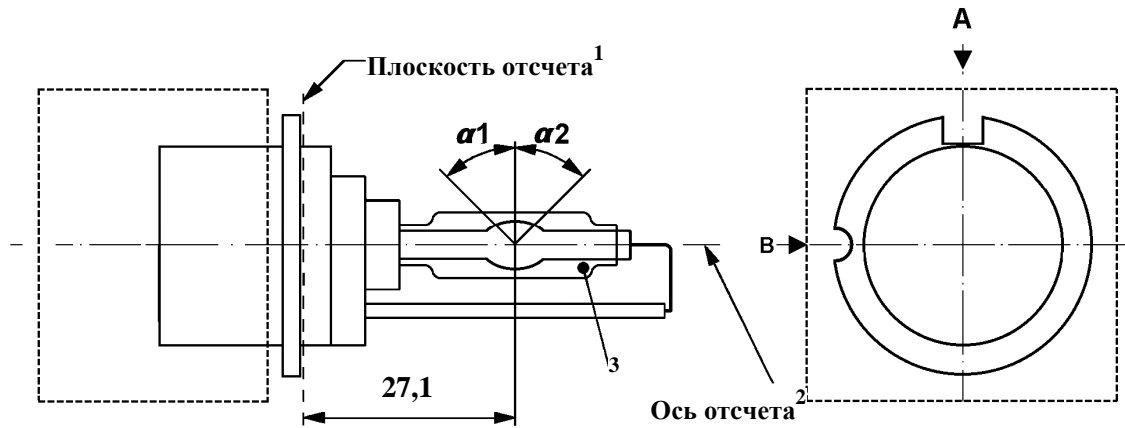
Категория D3S - Типовой газоразрядный источник света с пусковым приспособлением - Цоколь PK32d-5
